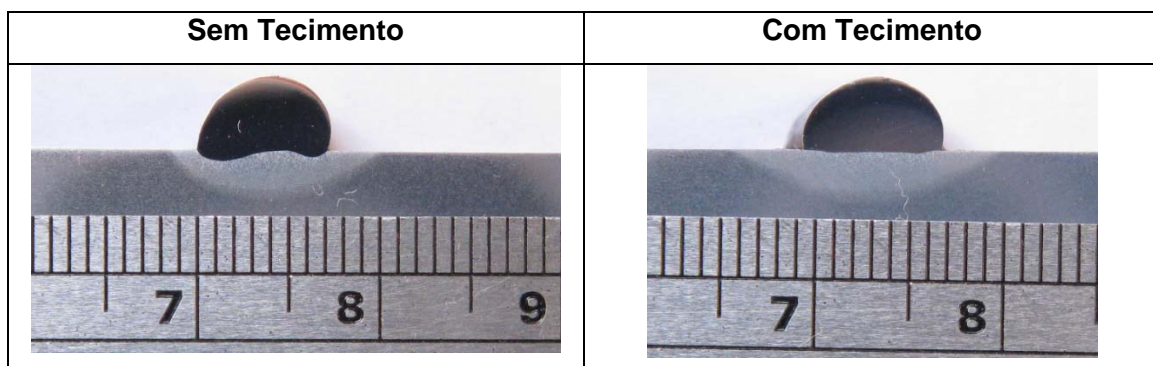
Seção transversal das amostras soldadas na condição CC2 com DPEP de 10 mm.
